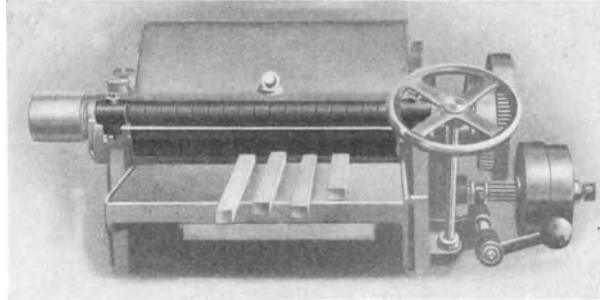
Schutzvorrichtung für Dicktenhobelmaschinen.
